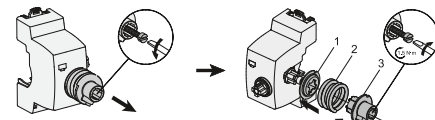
Монтаж поворотной рукоятки на боковой по распределительного шкафа / Figure 9 – Mounting the handle on the side of the distribution cabinet
